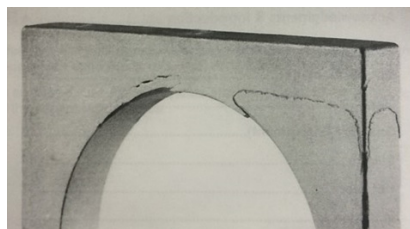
Exemplo de fissuração a quente [42]
